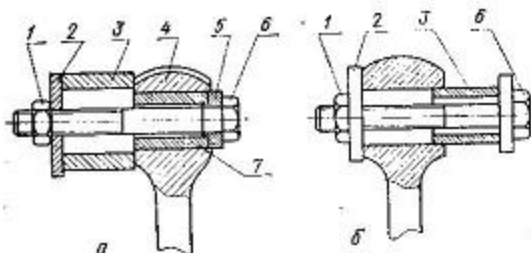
Выпрессовка и запрессовка втулки шатуна: а — выпрессовка; б — запрессовка
